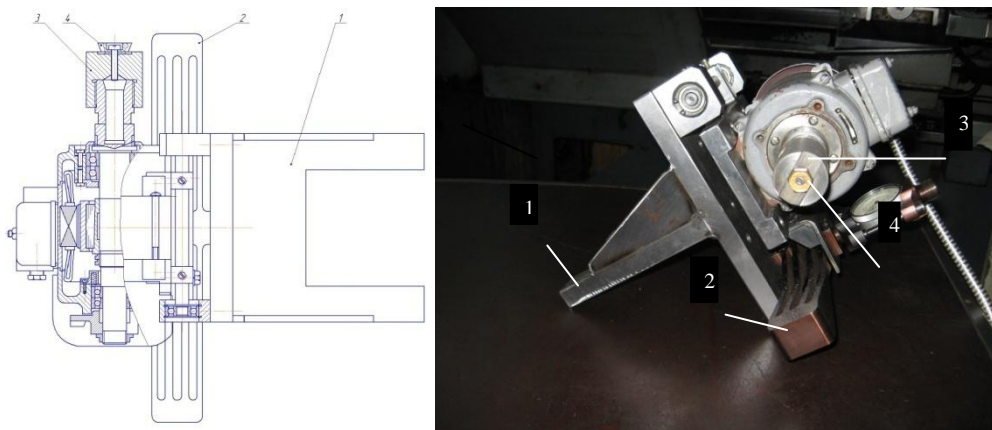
Измерительный инструментальный узел: 1 – кронштейн; 2 – динамометр; 3 – оправка; 4 – резец;
